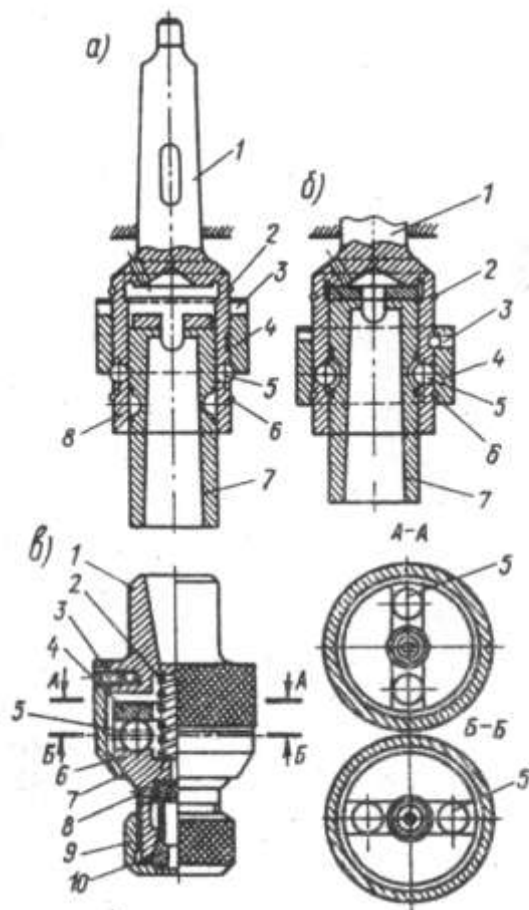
Быстросменный патрон для сверлильного станка с незажатой (а) и зажатой переходной втулкой (б); в — плавающий самоцентрирующий патрон для крепления метчиков
